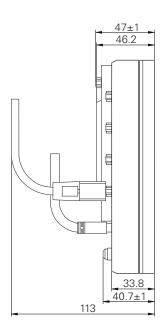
Размеры корпуса устройств с ID 1089182-хх
